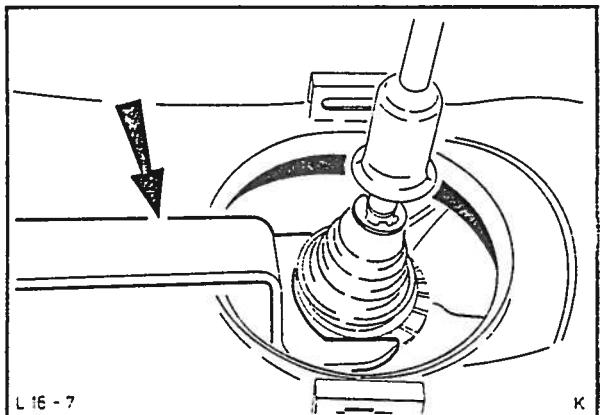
Demontering av gearspak med spesialverktøy 16-026.
